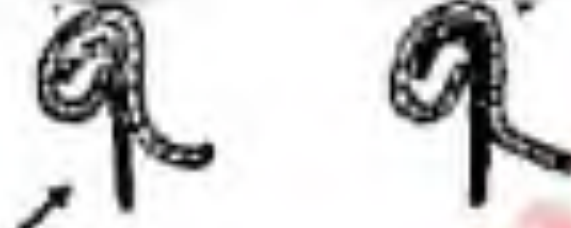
Вид в разрезе неправильной формы двойного шва, когда конец фланца корпуса банки согнут.
